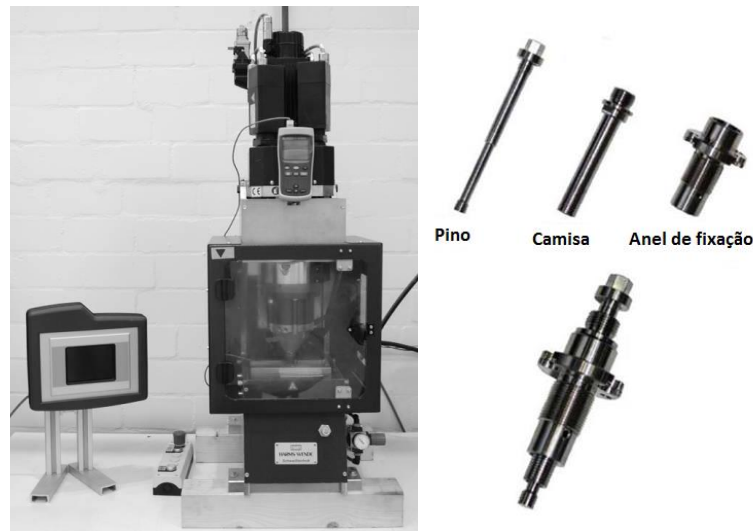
Máquina comercial RPS 100 desenvolvida em parceria com a empresa RIFTEC GmbH para realizar soldas FSpW e detalhes das ferramentas utilizadas na máquina para execução da solda.
